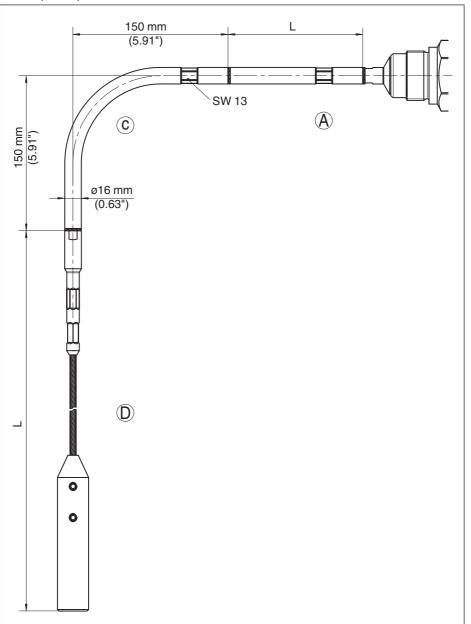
Segmento de arco ø 16 mm (0.63 in) con cable de extensión ø 6 mm (0.24 in)
